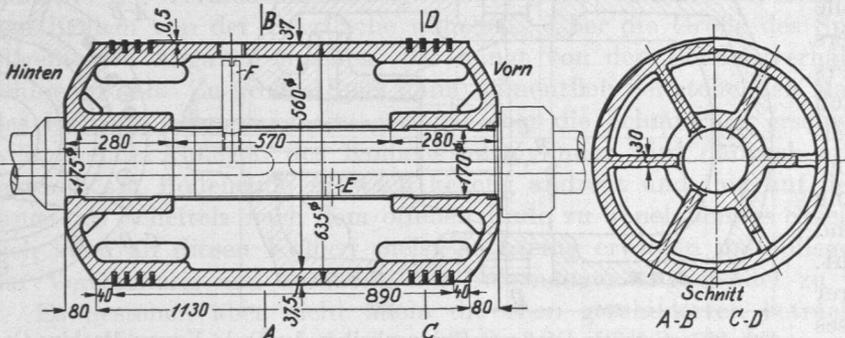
Kolben einer Zweitaktgasmaschine. Siegener Maschinenbau A.-G.
